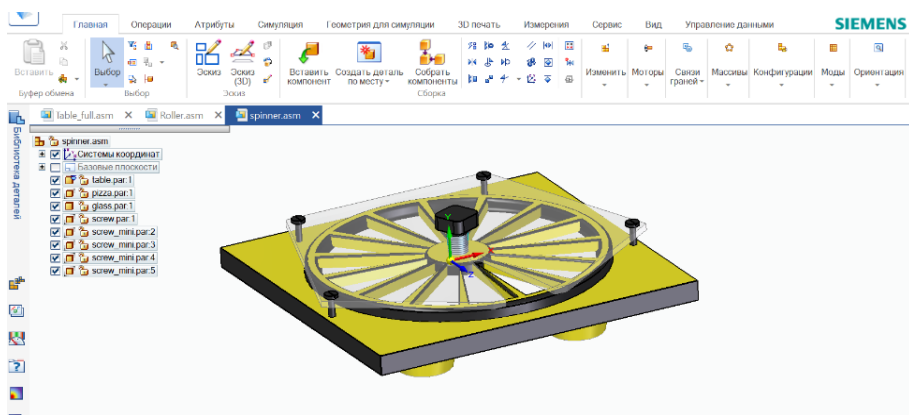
Карусельный питатель установщика SMP-330 на 24 ячейки
